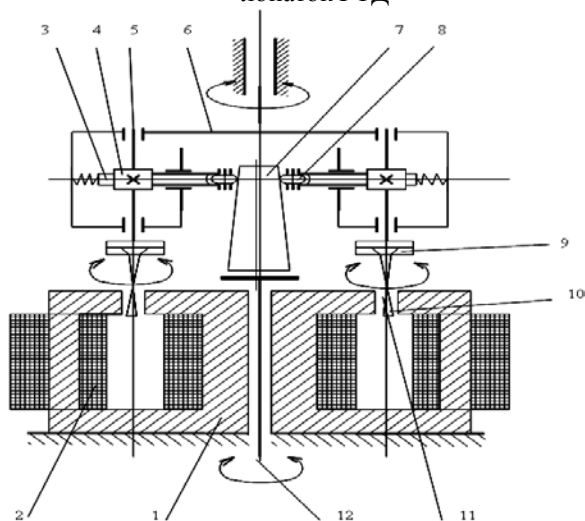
Схема установки для магнитно-абразивной обработки лопаток ГТД
